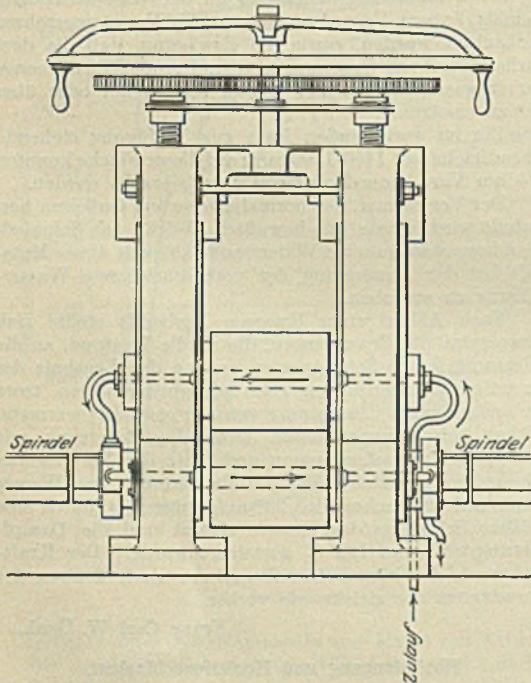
Kaltwalzgerüst mit wassergekühlten Walzen.
